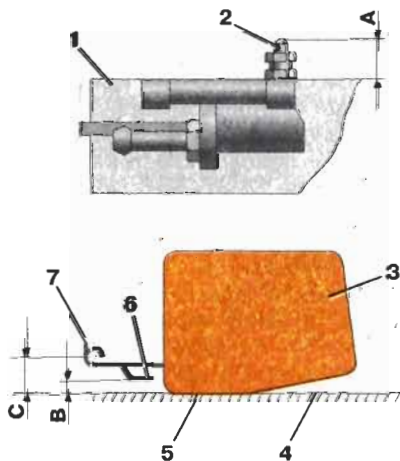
Схема регулировки уровня топлива в карбюраторе ДААЗ-1111: 1 - крышка карбюратора; 2 - топливный клапан; 3 - поплавок; 4 - установочная поверхность поворачивочной плиты; 5 - установочная поверхность поплавка; 6 - язычок кронштейна поплавка; 7 - ограничитель хода поплавка; А, В, С - контролируемые размеры
